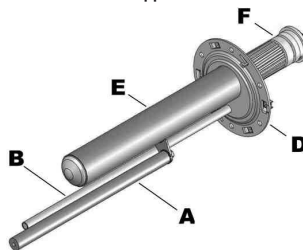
Стейтитовый нагревательный элемент + магниевый анод
